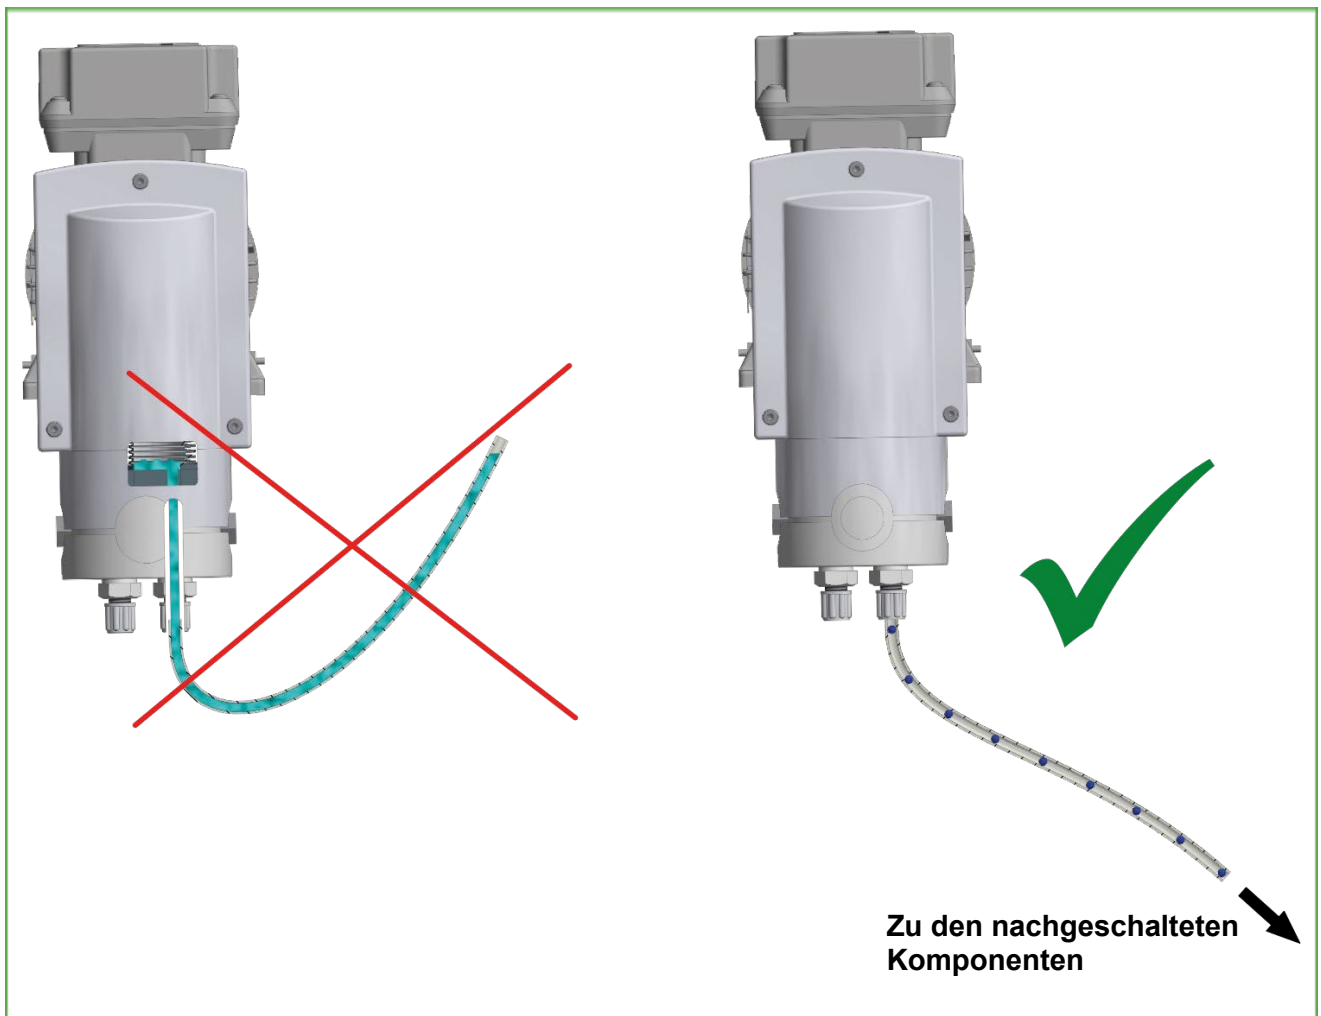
Gedrehter Pumpenkopf: Ausgangsschlauch mit Gefälle verlegen
